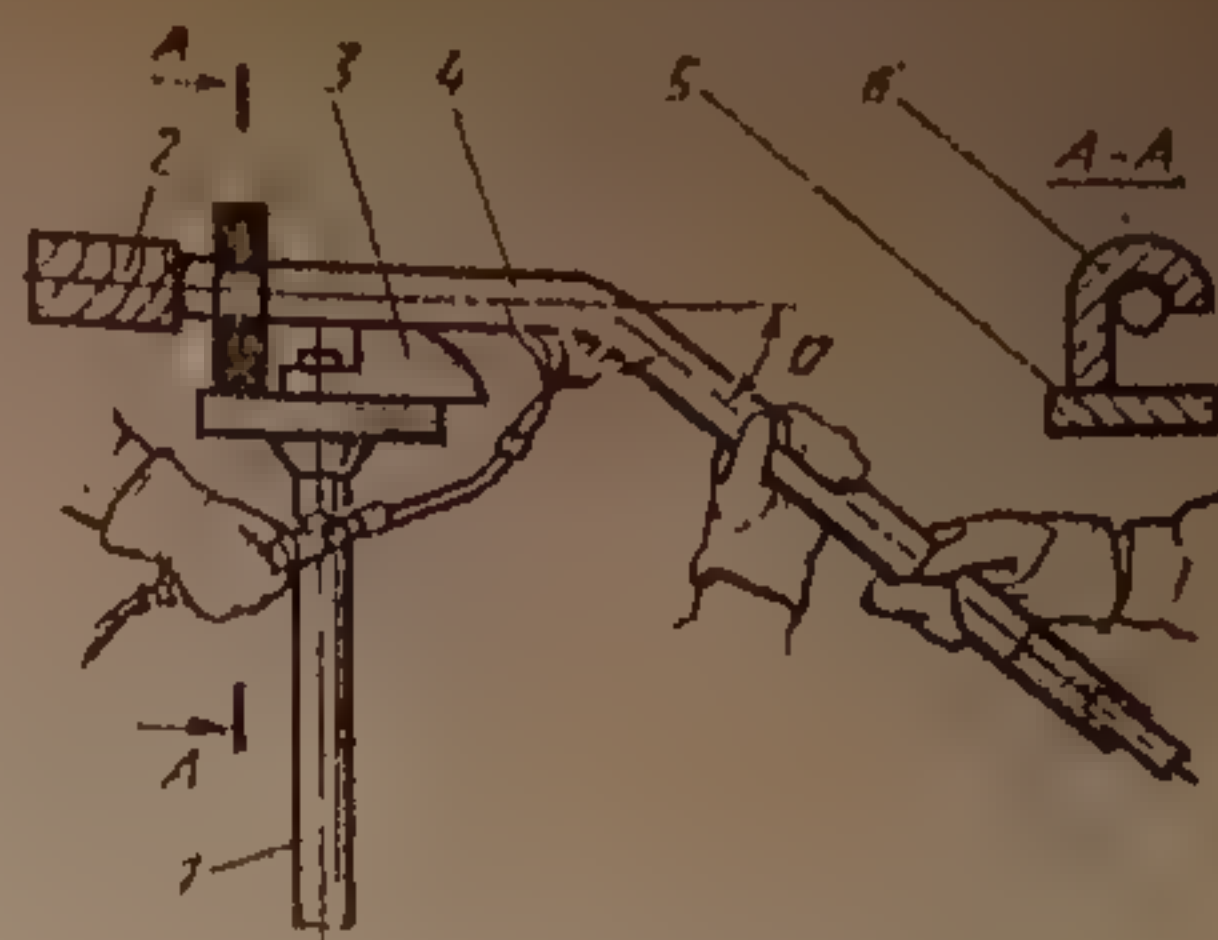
Гибка трубы в горячем состоянии на приспособлении: 1 — подставка; 2 — пробка; 3 — шаблон; 4 — изгибаемая труба; 5 — поперечина; 6 — упор
